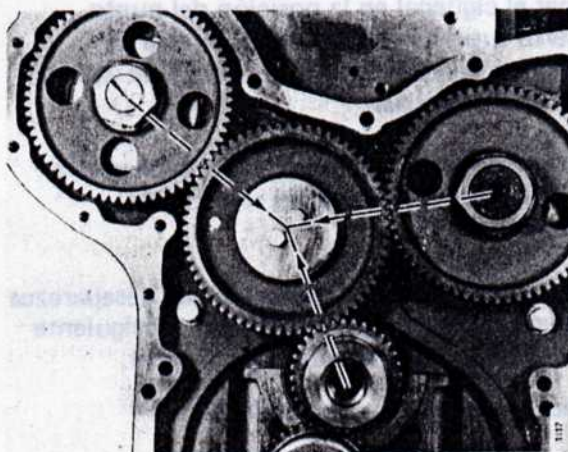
Sincronización de los engranajes antes de remover el engranaje intermedio
